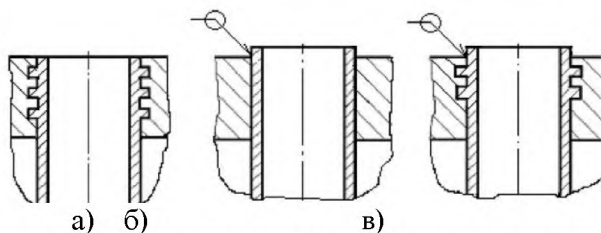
Крепление труб в трубных решетках: а – развальцовкой в канавки; б – сваркой; в – развальцовкой с подваркой
